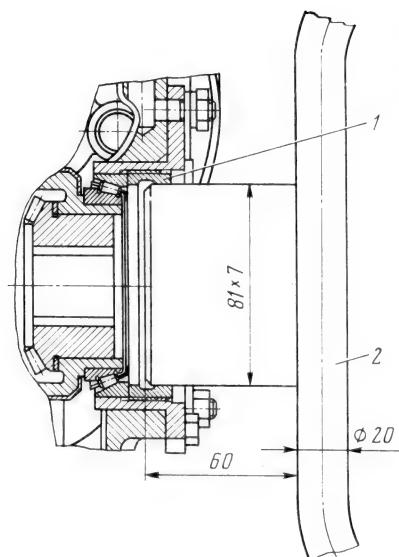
Ключ для заворачивания регулировочной гайки ведомой шестерни главной передачи;
